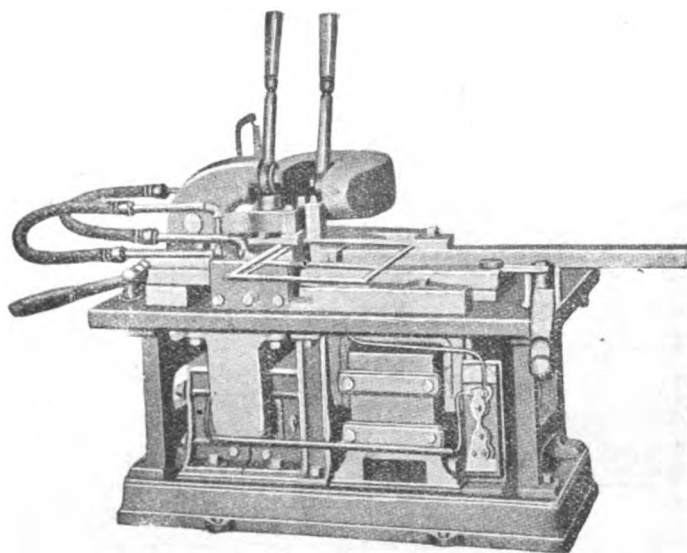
Macchina per saldature elettriche montata sul banco di lavoro.
